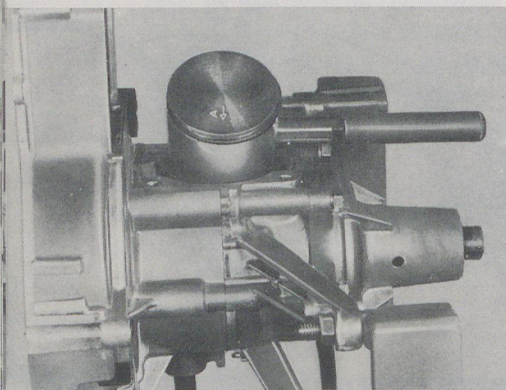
Aufsichten des Nockens auf die Kurbelwelle.
